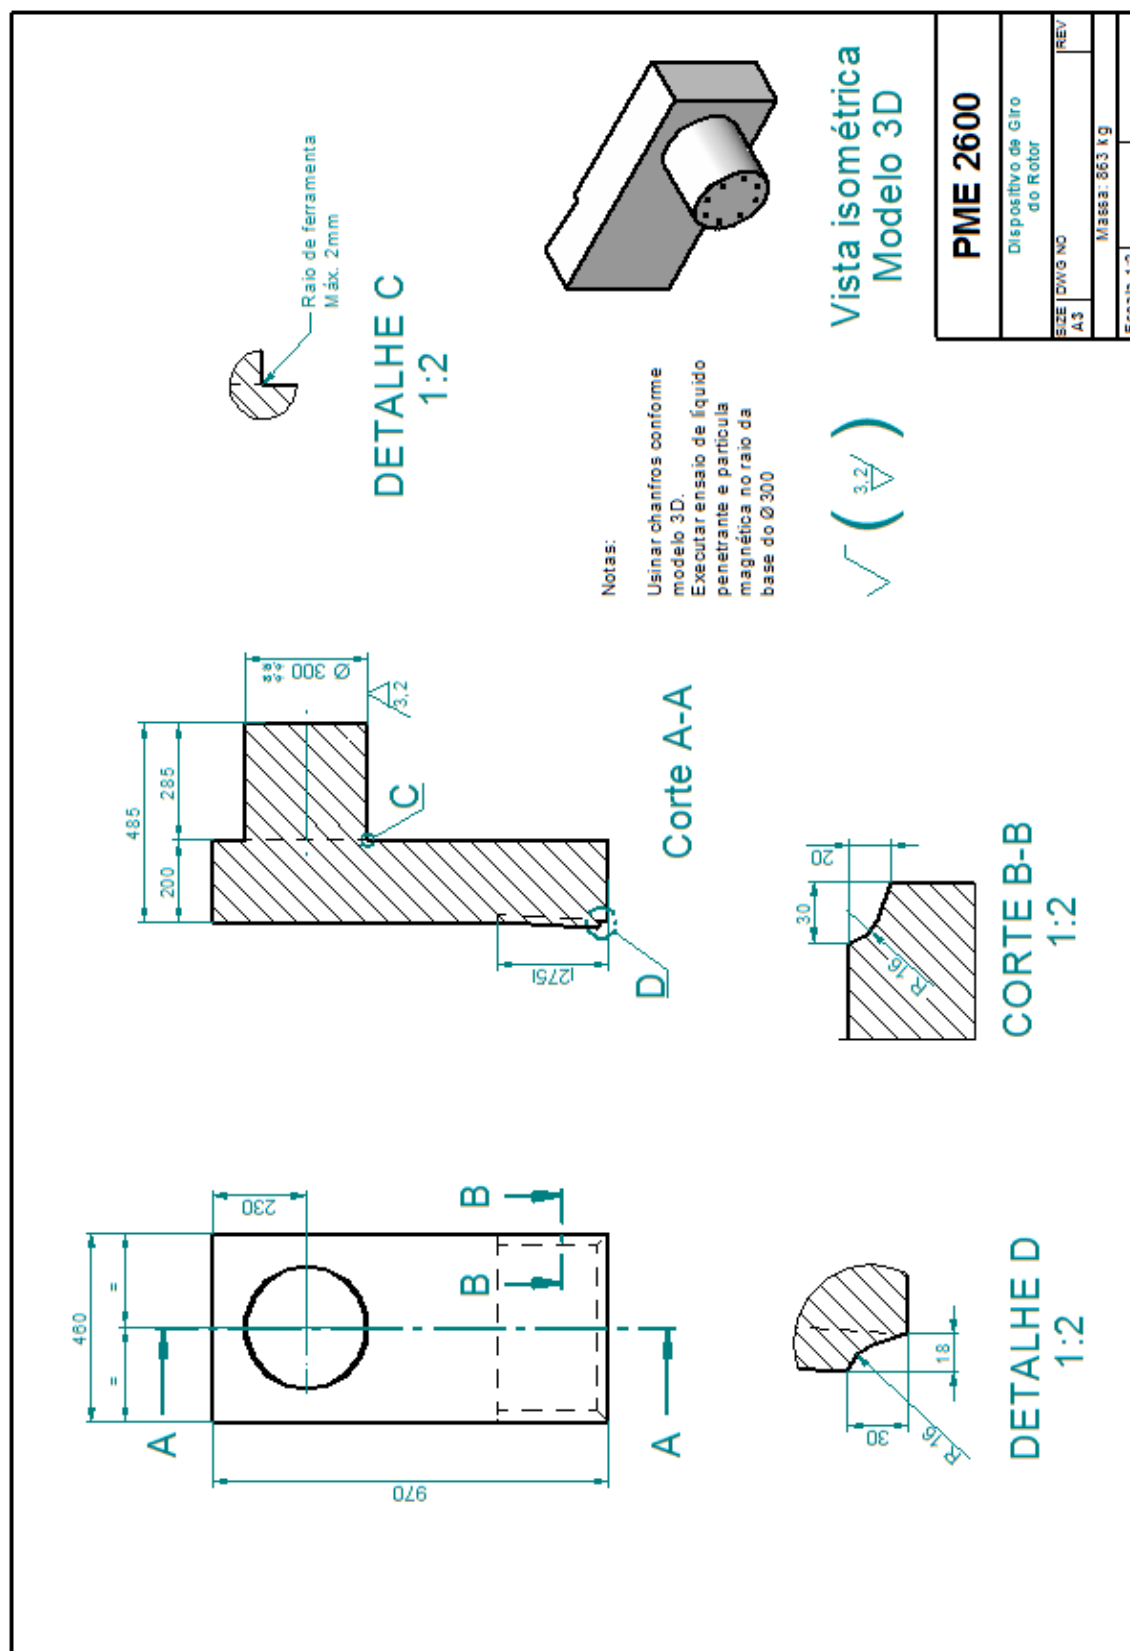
Desenho técnico de fabricação do bloco do dispositivo
